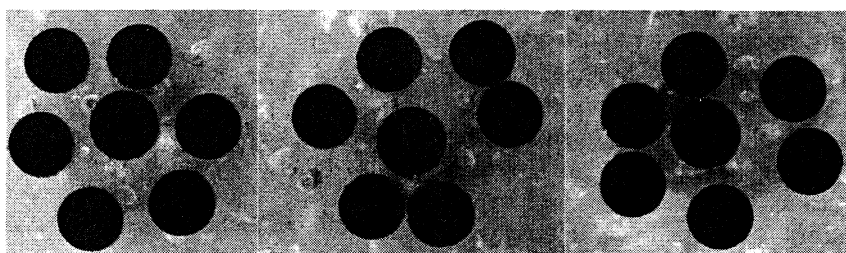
Поперечное расположение проволок металлокорда конструкции 0,40+6x0,38 HT FRP
